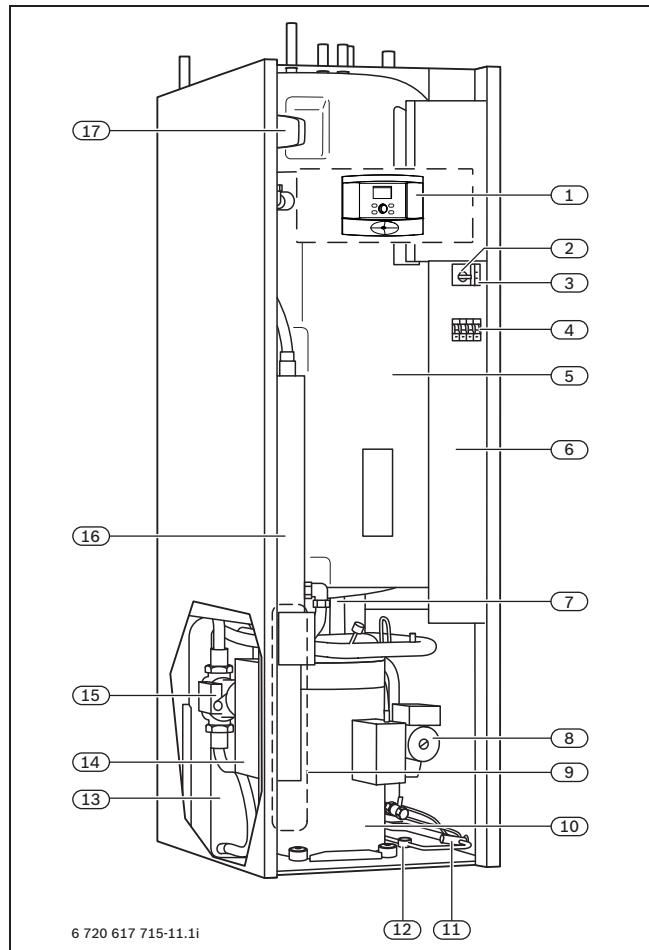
Ausgewählte Bauteile und Baugruppen STM 60 ... STM 110
